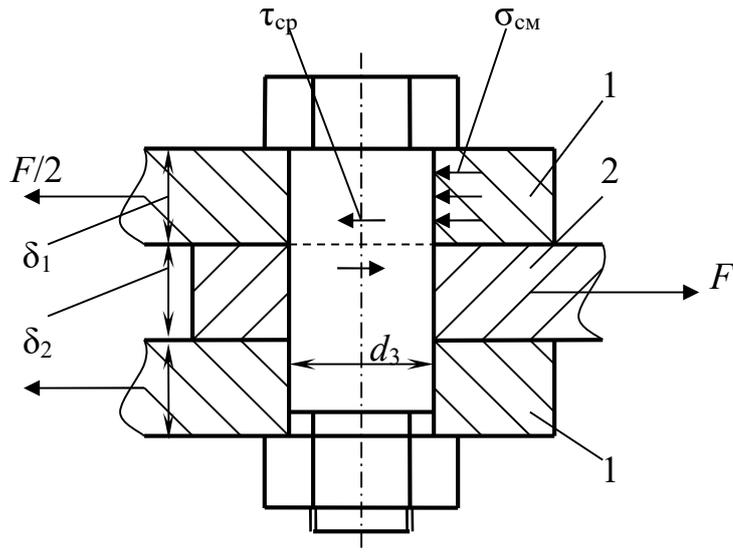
Соединение, нагруженное поперечными силами (болт в отверстии без зазора)
